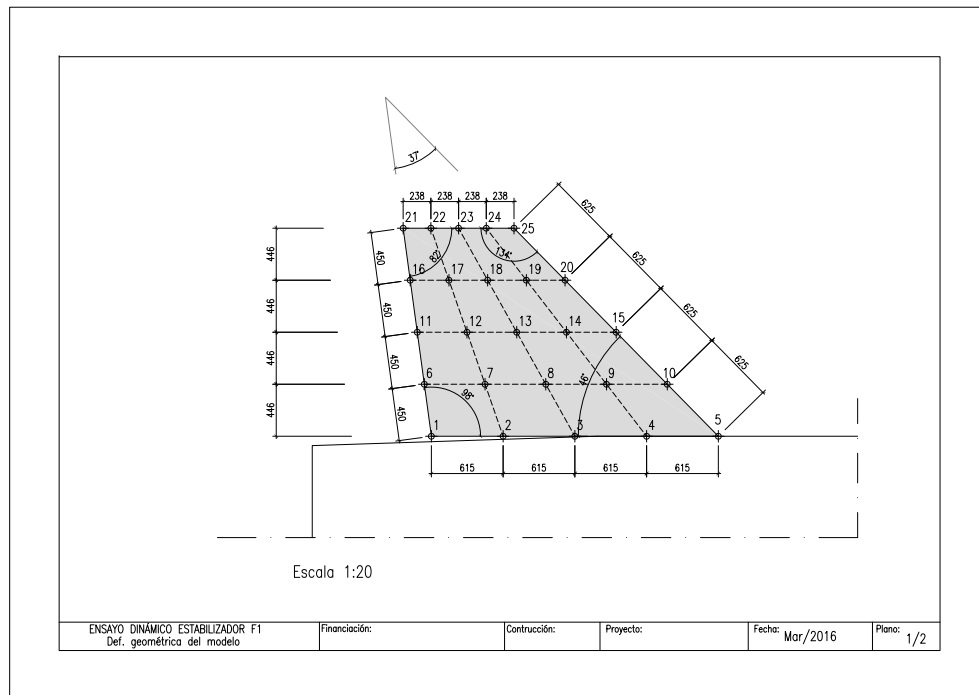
Plano del estabilizador Mirage F1, cotas en milímetros
